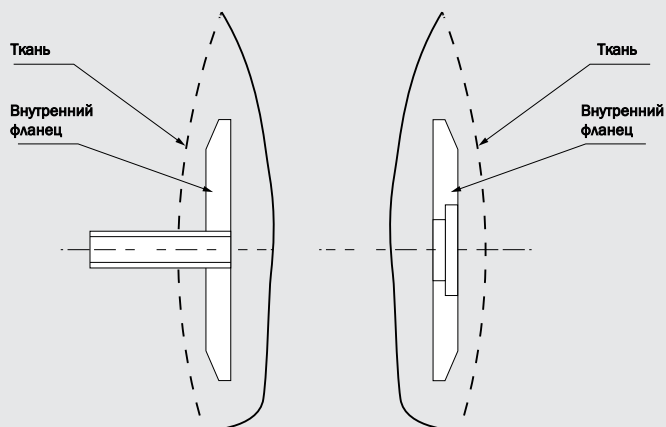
Внутренний фланец и наложение корда на него. Поднять слои корда шины невозможно
